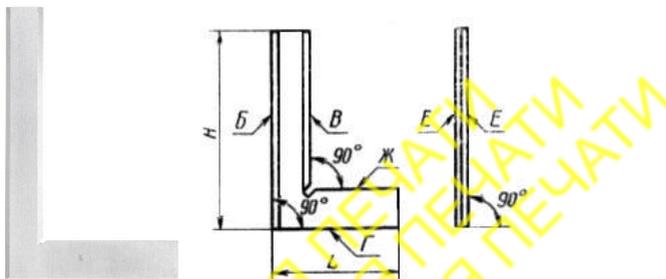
Общий вид угольников типа УЛП и обозначение условных размеров
